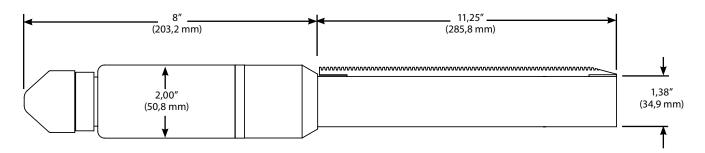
Dimensions de la torche en ligne PT-26 « SL »
